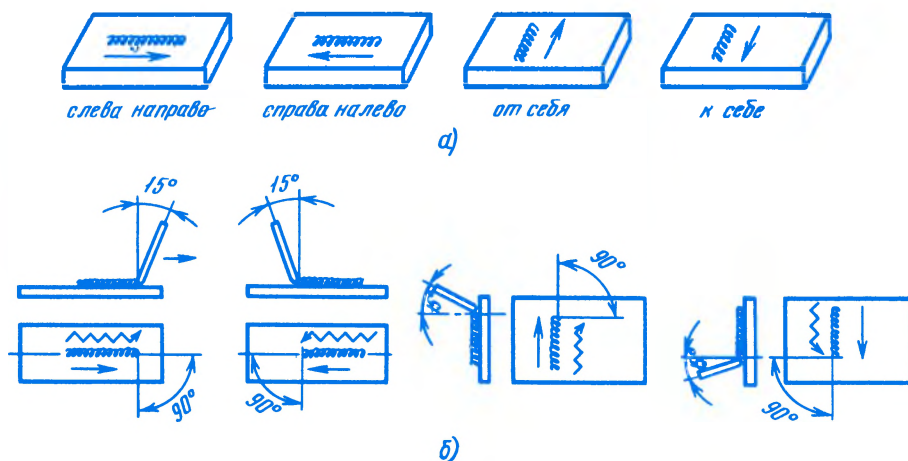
Направления сварки (а) и наклон электрода (б)
